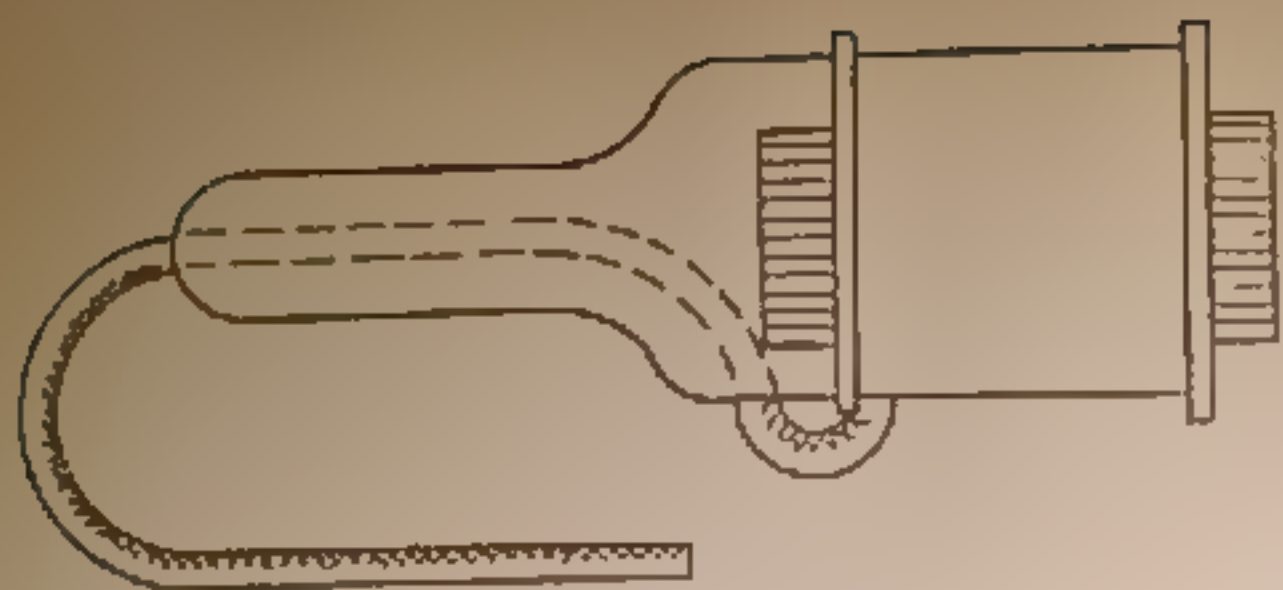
Конструкция ручного разматывающего электромагнита
